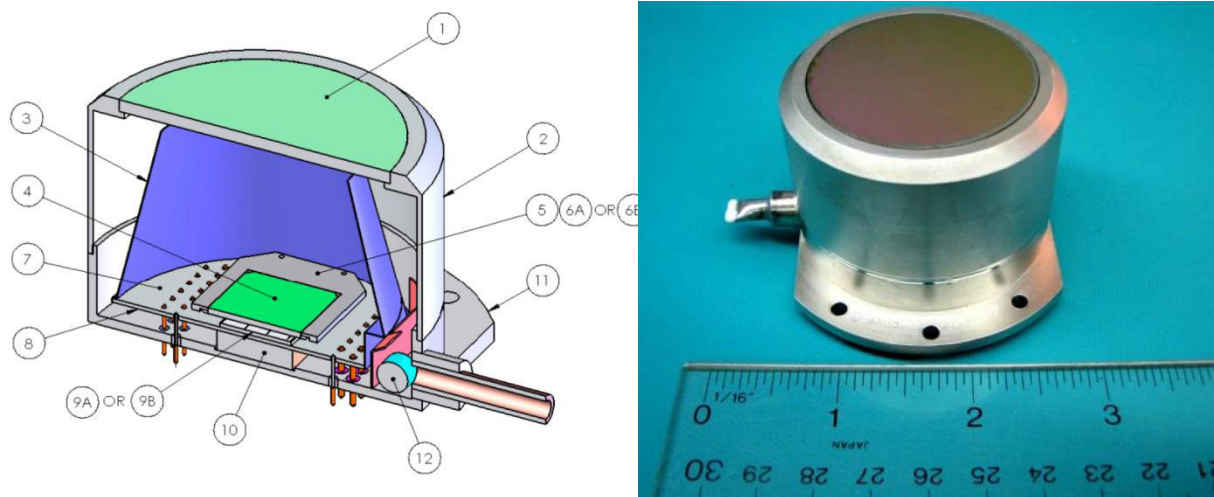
Конструкция и внешний вид корпуса микроболометрического фотоприёмника с встроенной охлаждаемой термостабилизированной блендой.
